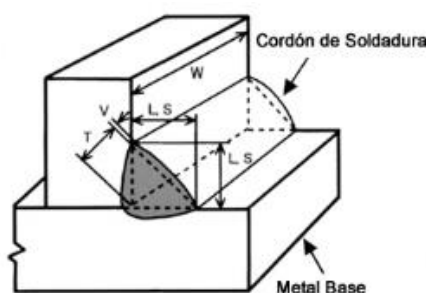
Esquema de cordón de soldadura para la unión de tubos.
